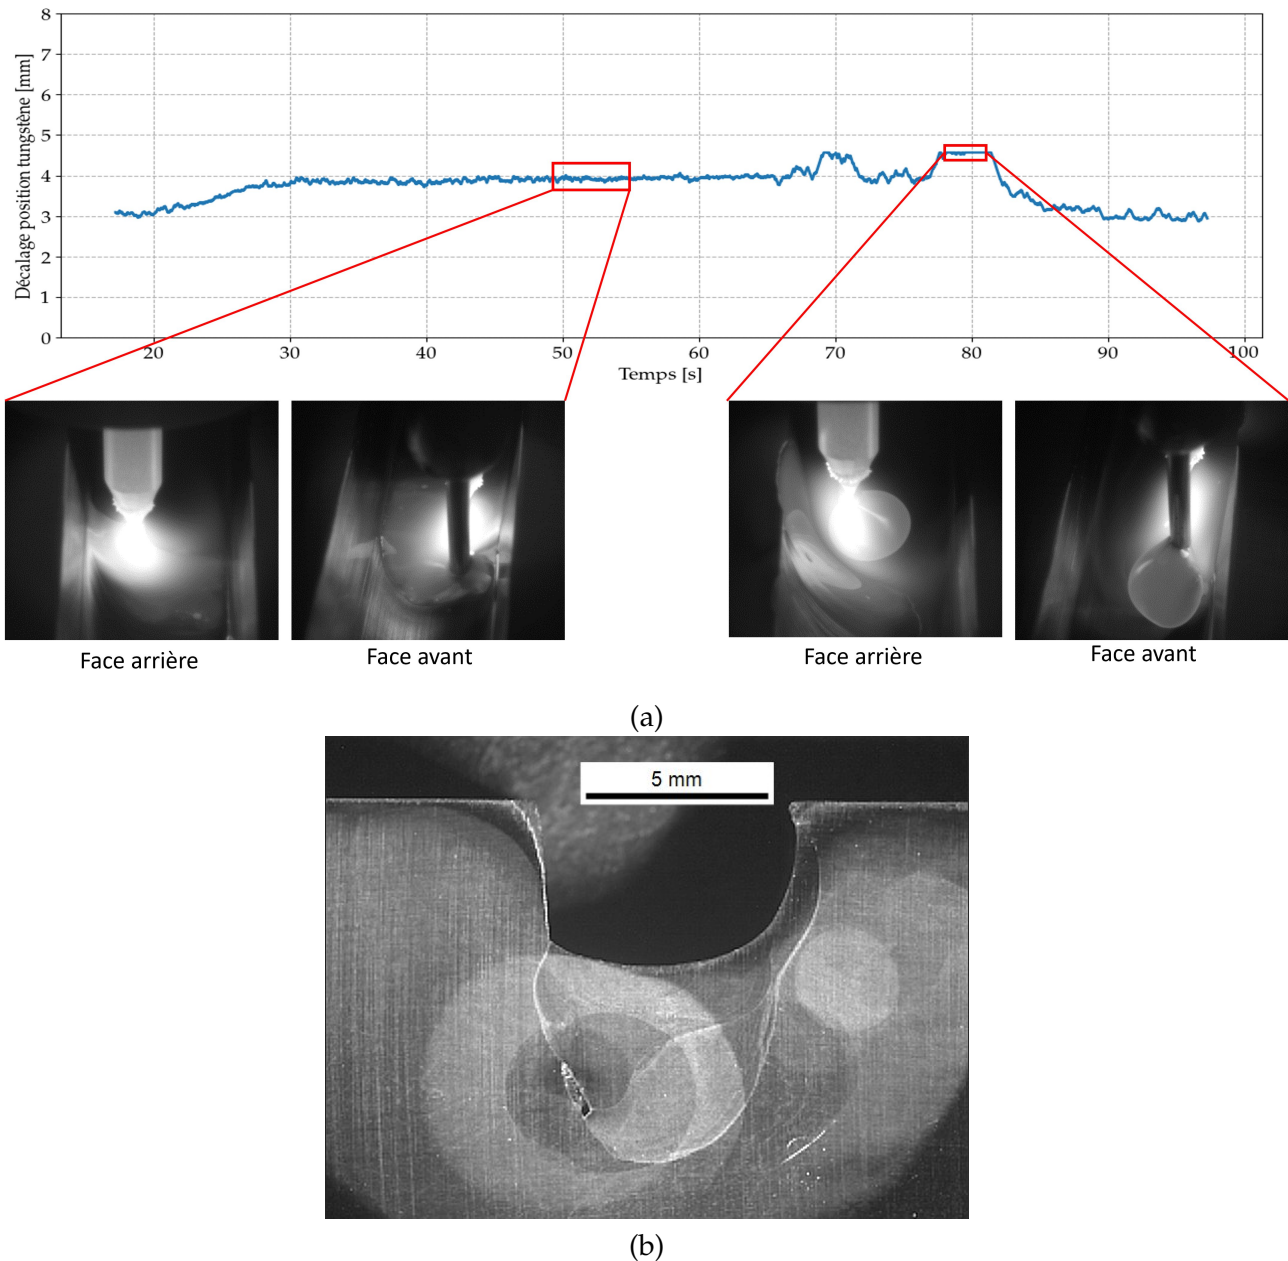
(a) Exemple de résultat suite à l'étude des limites du décalage de torche de soudage dans le chanfrein étroit, (b) coupe macrographique pour cette configuration lors du soudage de la deuxième passe.
